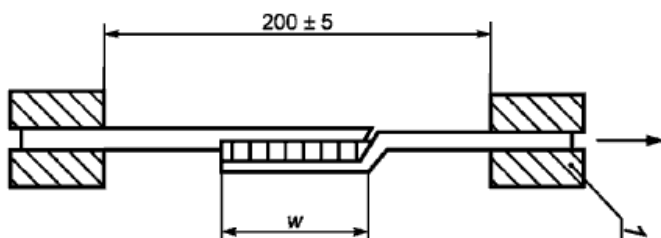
Образцы для испытаний на раздир сварного соединения:
